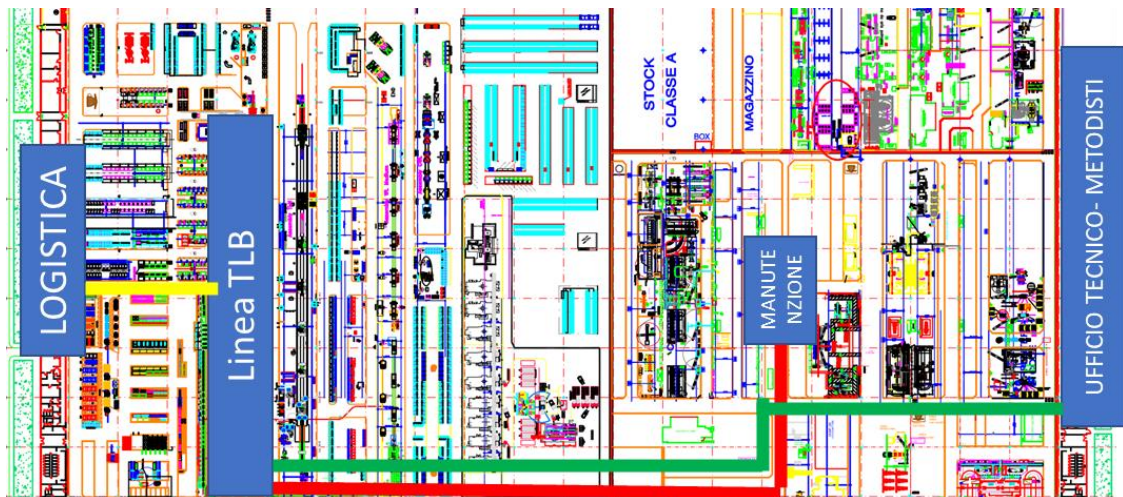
PLANIMETRIA DELLO STABILIMENTO CON LO “SPAGHETTI CHART” DEGLI SPRECHI
